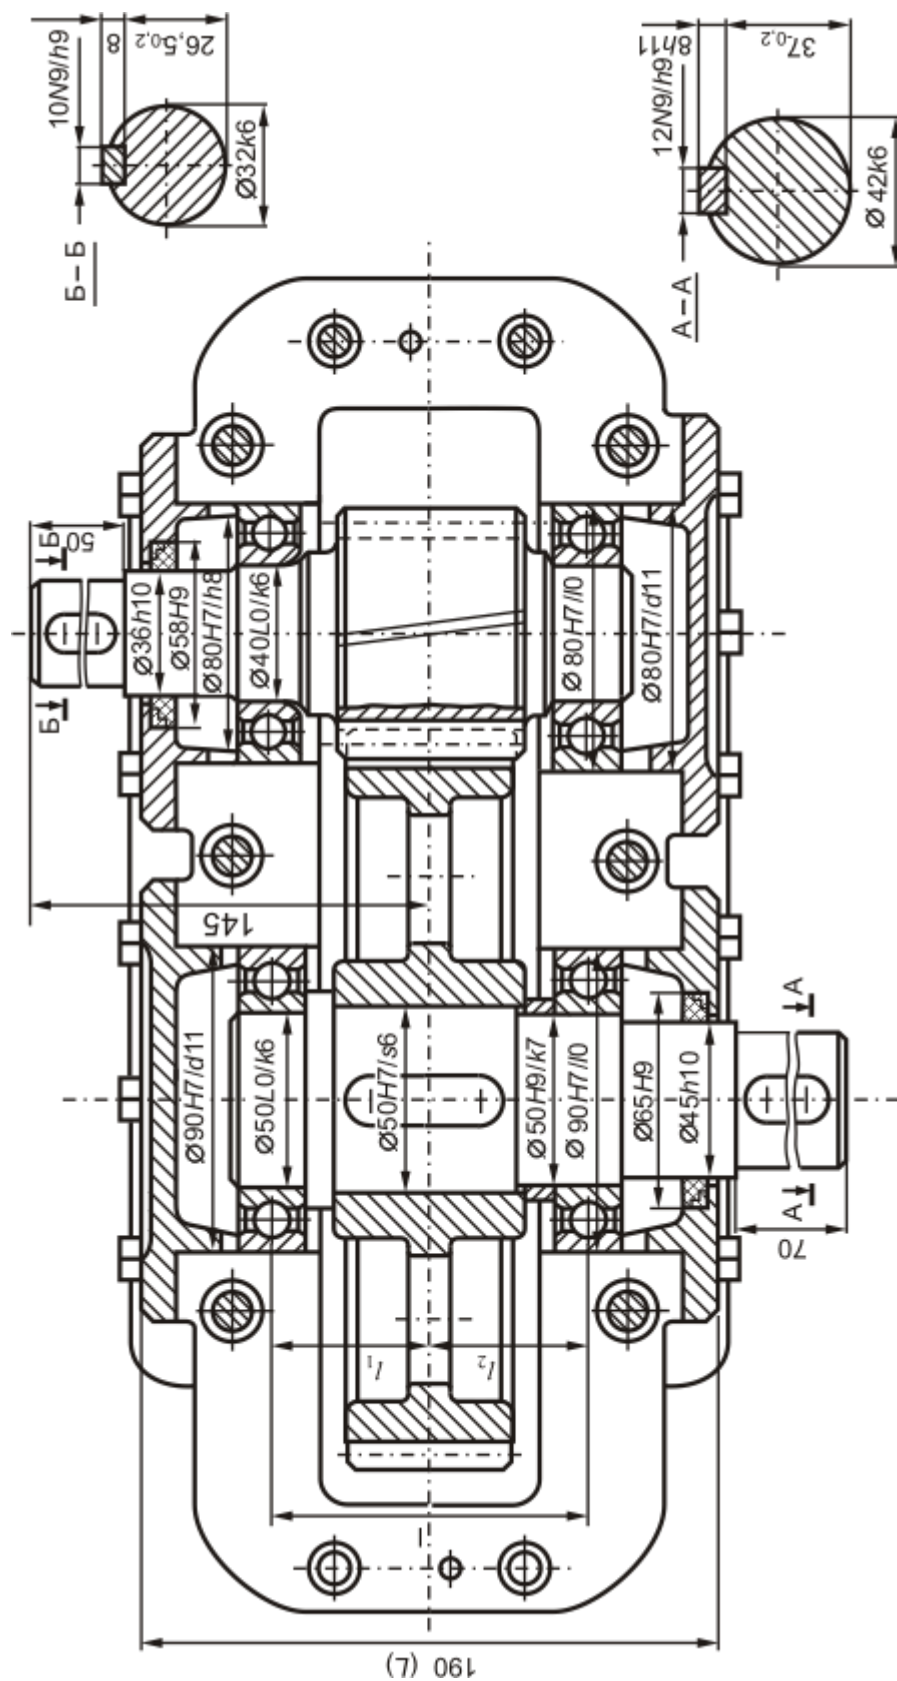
Одноступенчатый цилиндрический редуктор.
